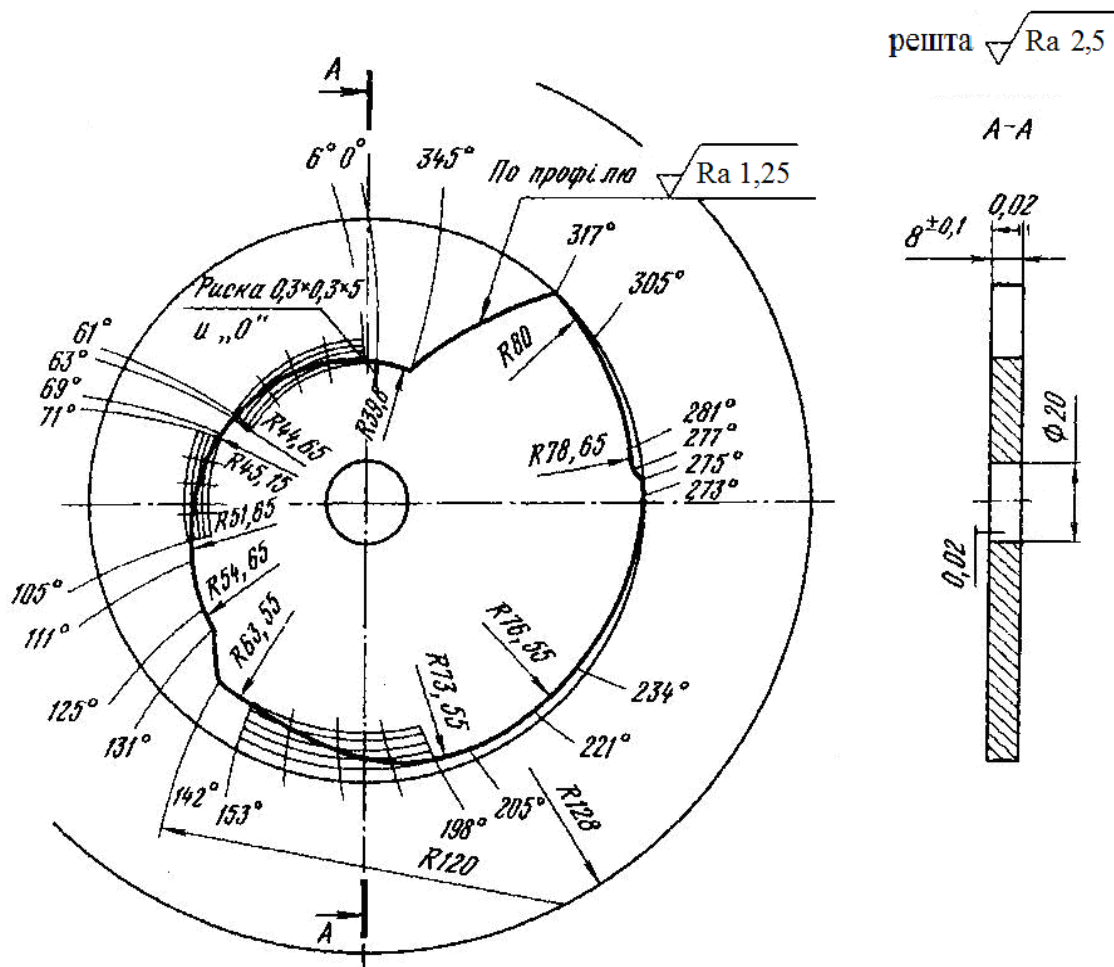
Креслення кулачка шпindelної бабки
